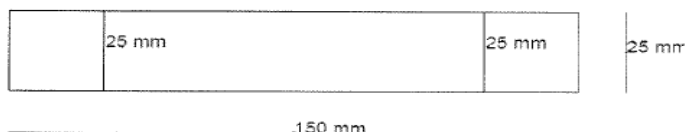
Dimensiones de la probeta para el ensayo de tensión
